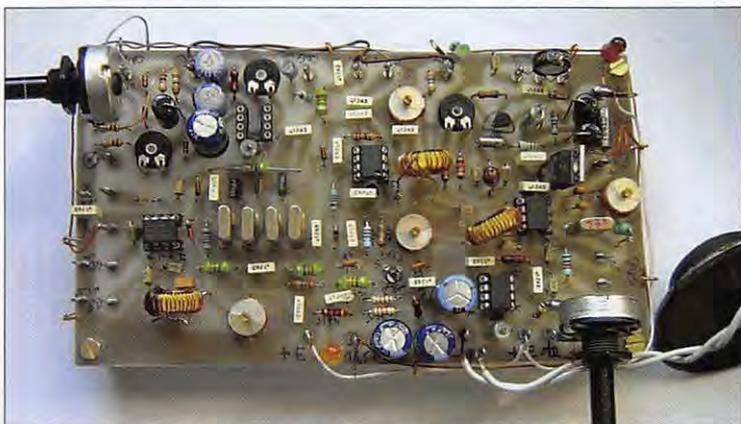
Vue de la platine du générateur SSB BINGO au cours des essais.
